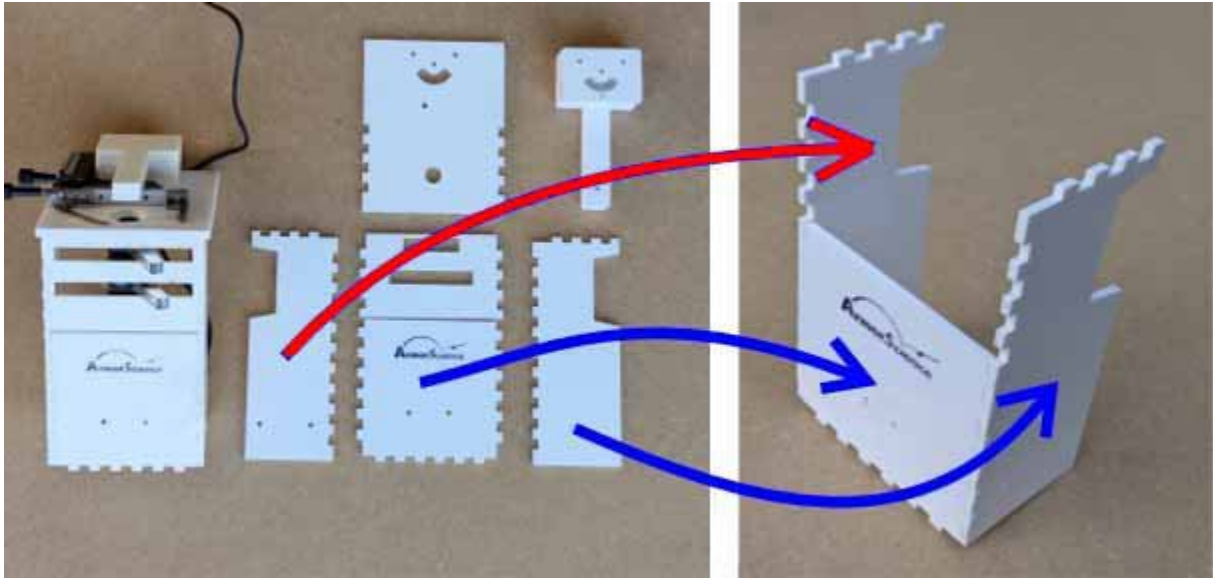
Début du montage du châssis interne. Trois pièces constituent la partie basse.
